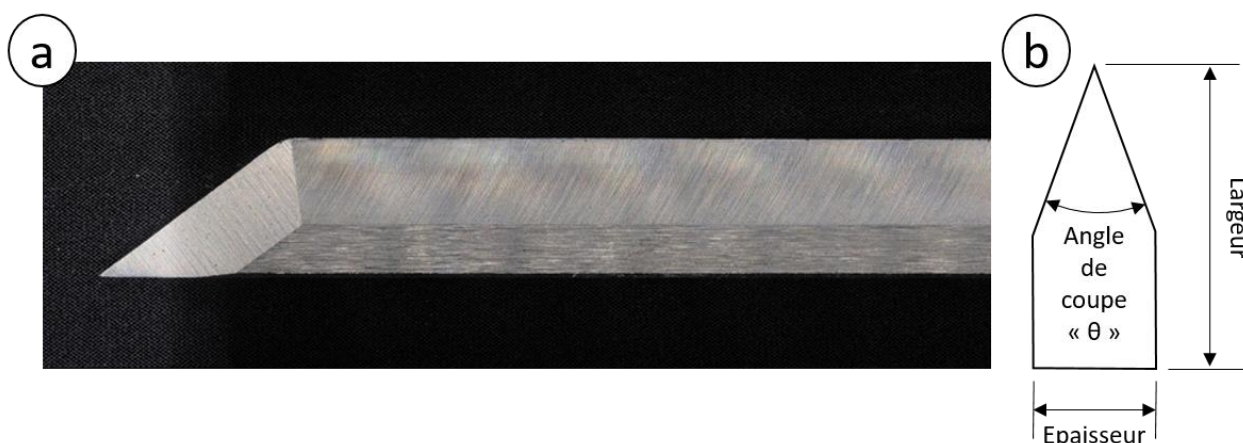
(a) Lame lisse de coupe ; (b) profil de coupe (section de lame).
